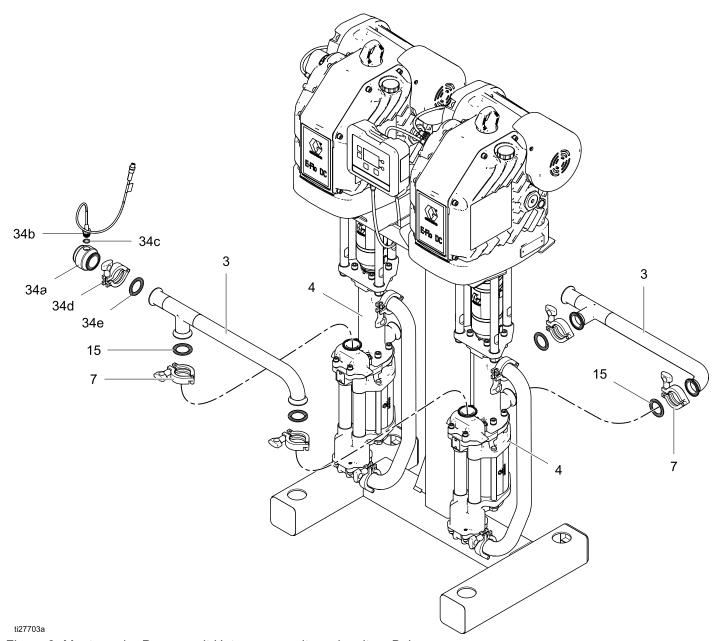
Montage der Pumpe, mit Unterpumpe mit versiegeltem Balg
